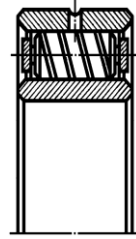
Схема роликового радіального підшипника з витими роликами
